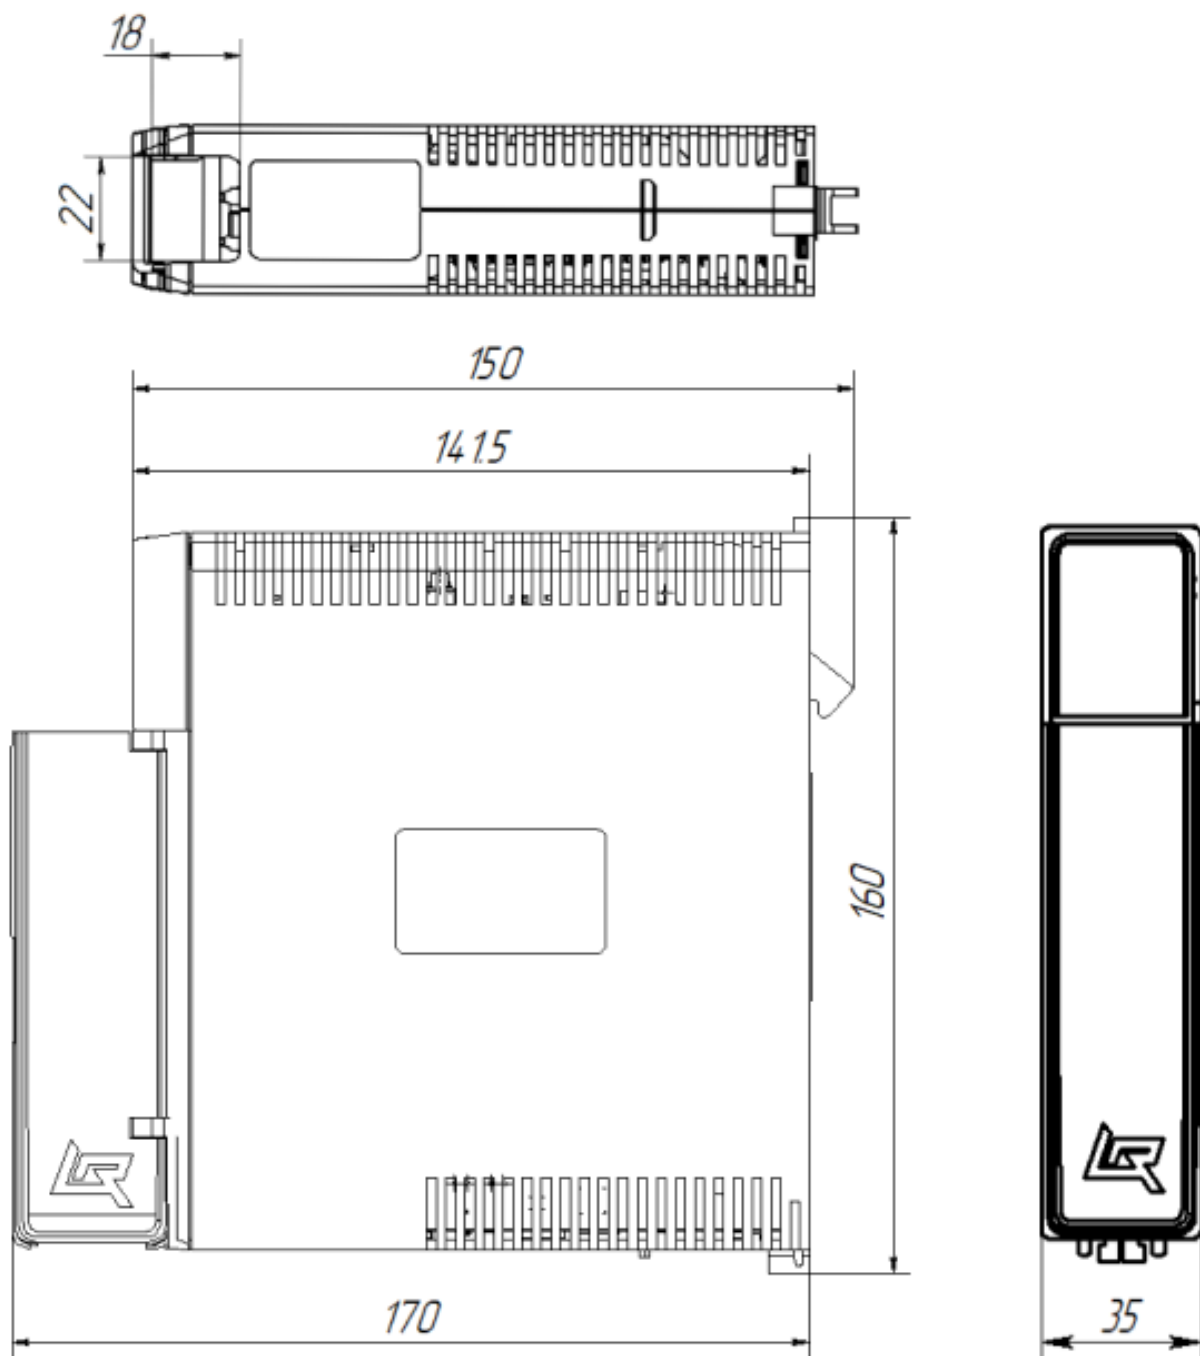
Габаритные и присоединительные размеры модуля расширения в пластмассовом корпусе
